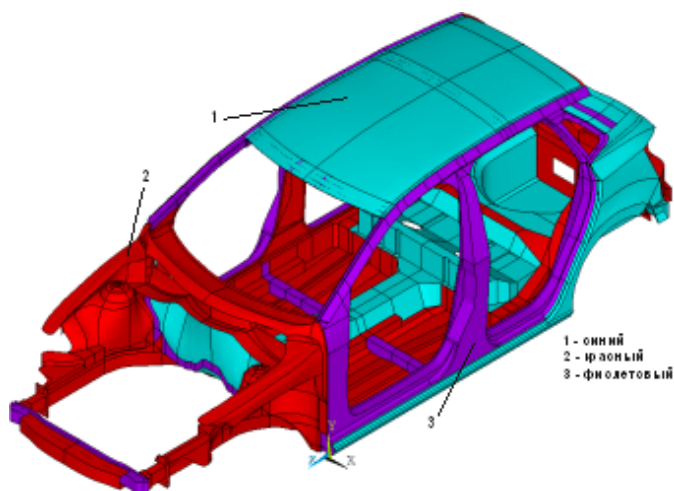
Схема кузова легкового автомобиля, изготовленного из различных марок сталей
